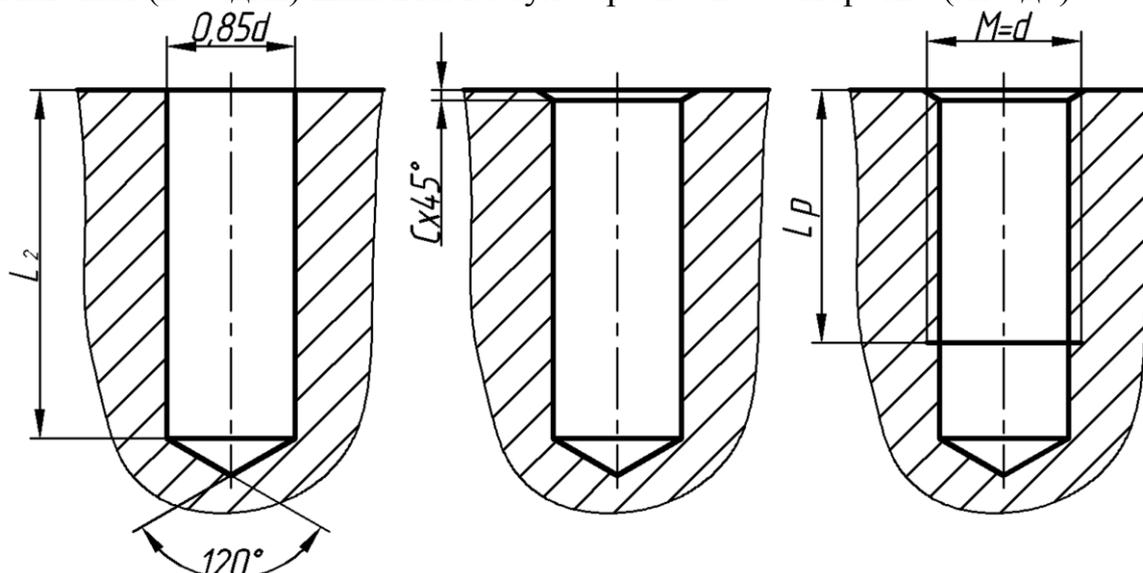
Отверстие с резьбой для шпилечного и винтового соединений
